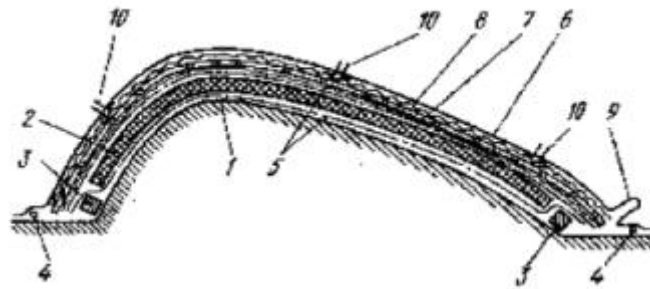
Схема вакуумного формування деталей з ПКМ
